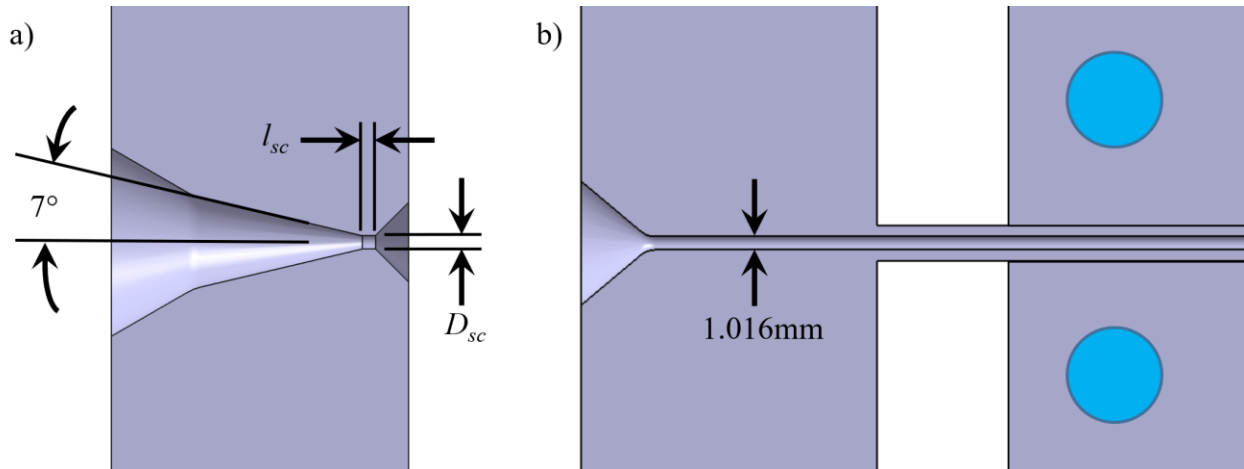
Géométrie des surfaces de moulage typique des filières. a) Filière chauffante. b) Filière refroidissante et tube de refroidissement de 75mm
